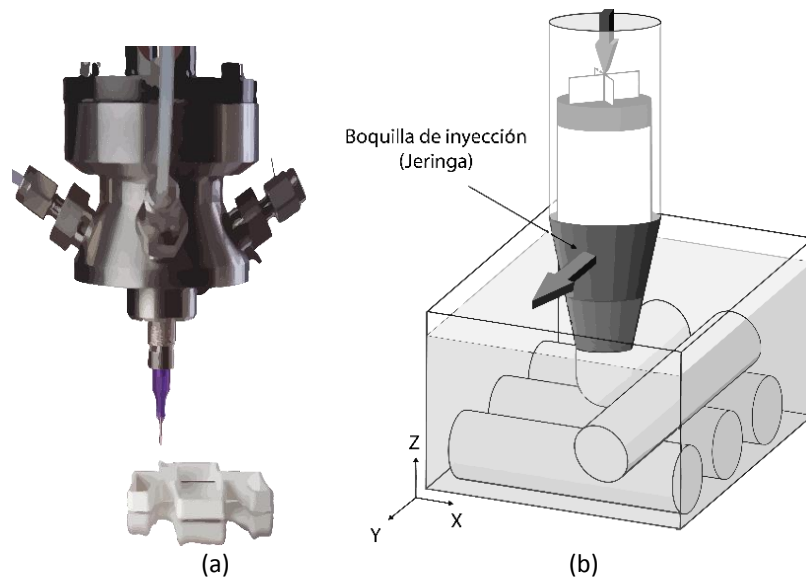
Boquilla de inyección del sistema Robocasting; (a) fotografía del cabezal inyector; (b) esquema del proceso Robocasting.
